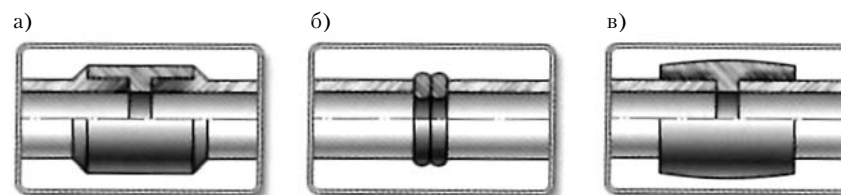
Сварное соединение труб: а) муфтовое; б) стыковое; в) при помощи фитинга для терморезисторной сварки [2]
